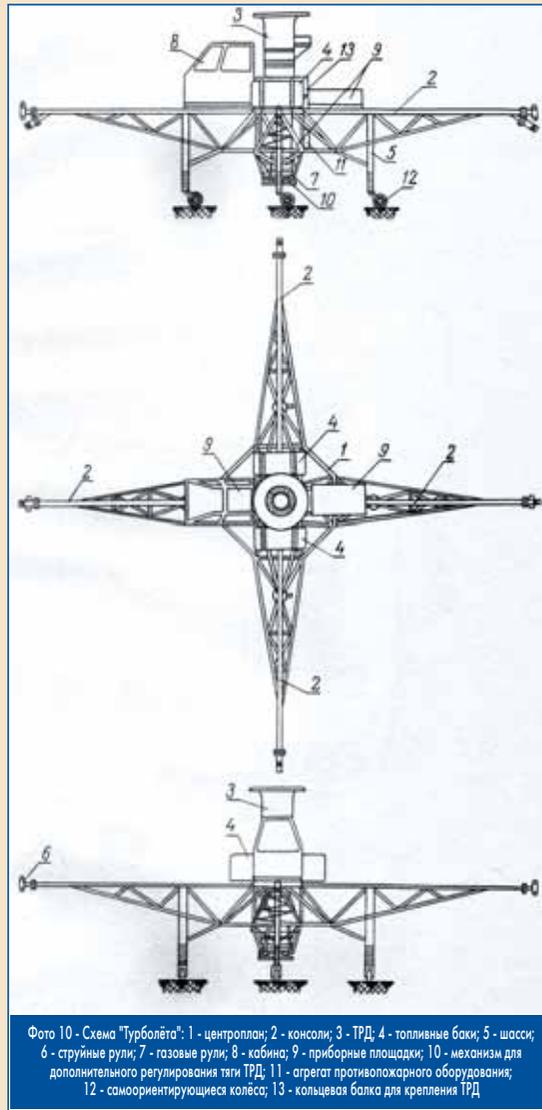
Схема "Турболёта": 1 - центроплан; 2 - консоли; 3 - ТРД; 4 - топливные баки; 5 - шасси; 6 - струйные рули; 7 - газовые рули; 8 - кабина; 9 - приборные площадки; 10 - механизм для дополнительного регулирования тяги ТРД; 11 - агрегат противопожарного оборудования; 12 - самоориентирующиеся колёса; 13 - кольцевая балка для крепления ТРД
